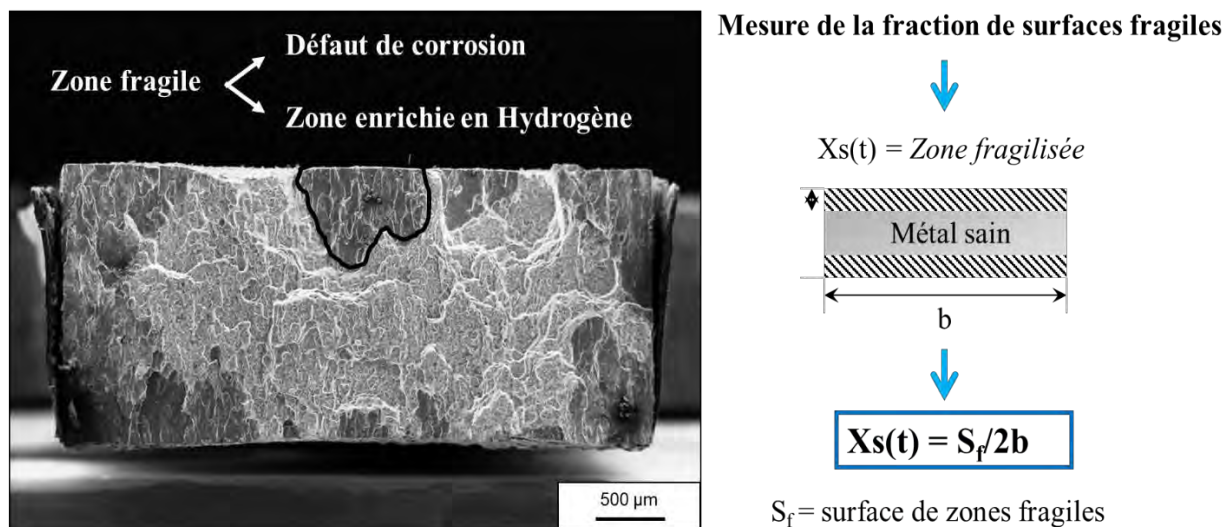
Principe de mesure de l'endommagement en corrosion par analyse fractographique
